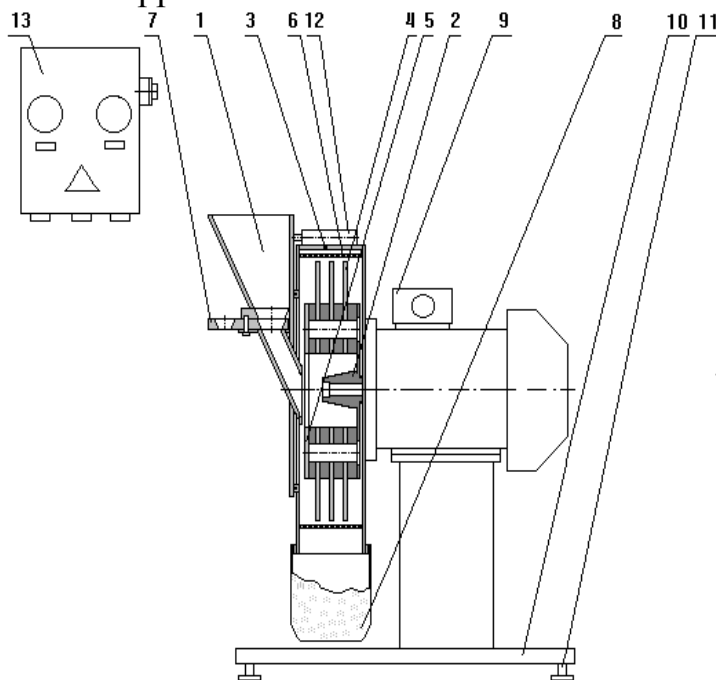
Схема модернизированного измельчителя пряно-ароматических растений: 1 – дверца с бункером; 2 – ротор; 3 – корпус; 4 – молоток; 5 – кольцо; 6 – решето; 7 – диск; 8 – мешок; 9 – электродвигатель; 10 – станина; 11 – опора; 12 – выключатель; 13 – пульт управления.
